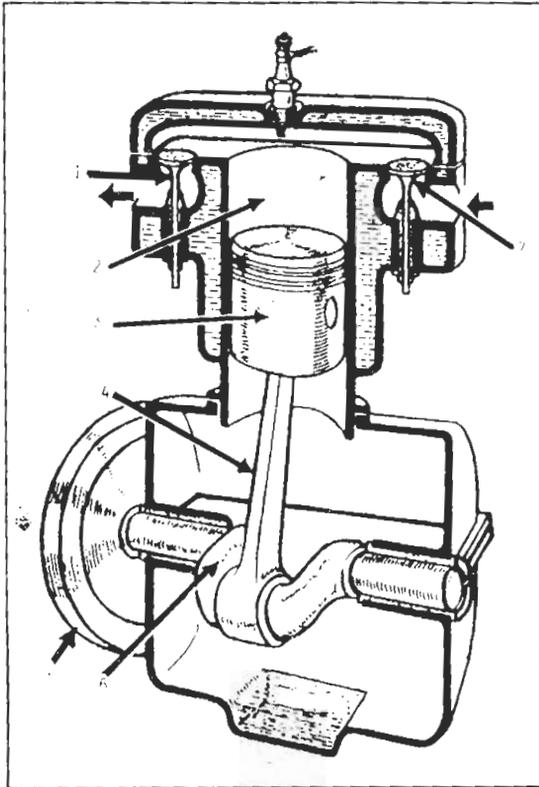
Motor de combustión interna con ciclo de explosión a cuatro tiempos. 1.- Válvula de escape. 2.- Cilindro. 3.- Pistón o émbolo. 4.- Biela. 5.- Volante. 6.- Cigüeñal. 7.- Válvula de admisión.
